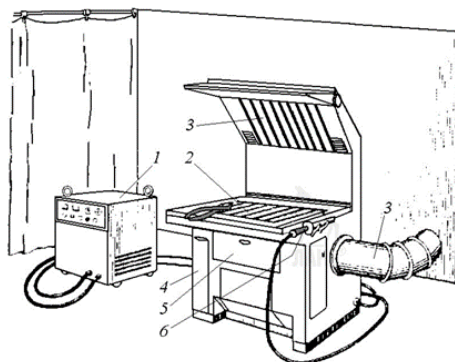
Стационарный пост для ручной дуговой сварки
